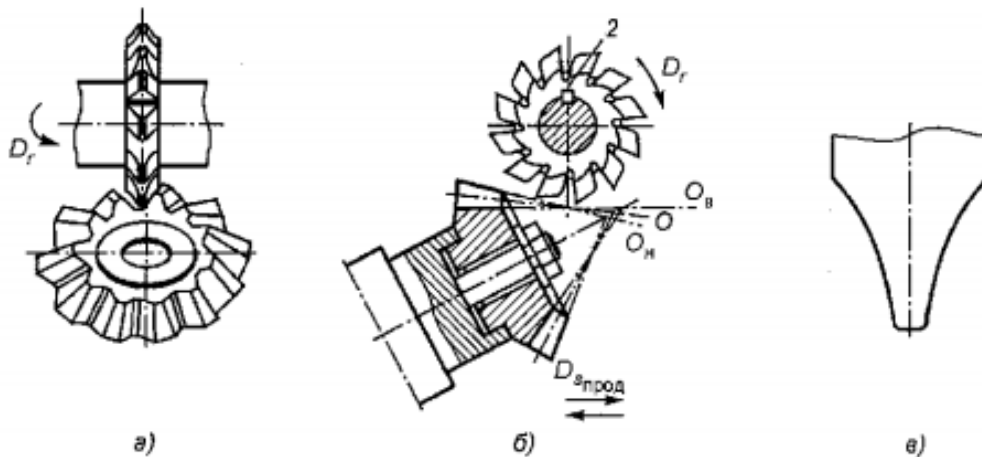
Схема нарізання прямозубого конічного колеса дисковою модульною фрезою в один чистовий робочий хід
